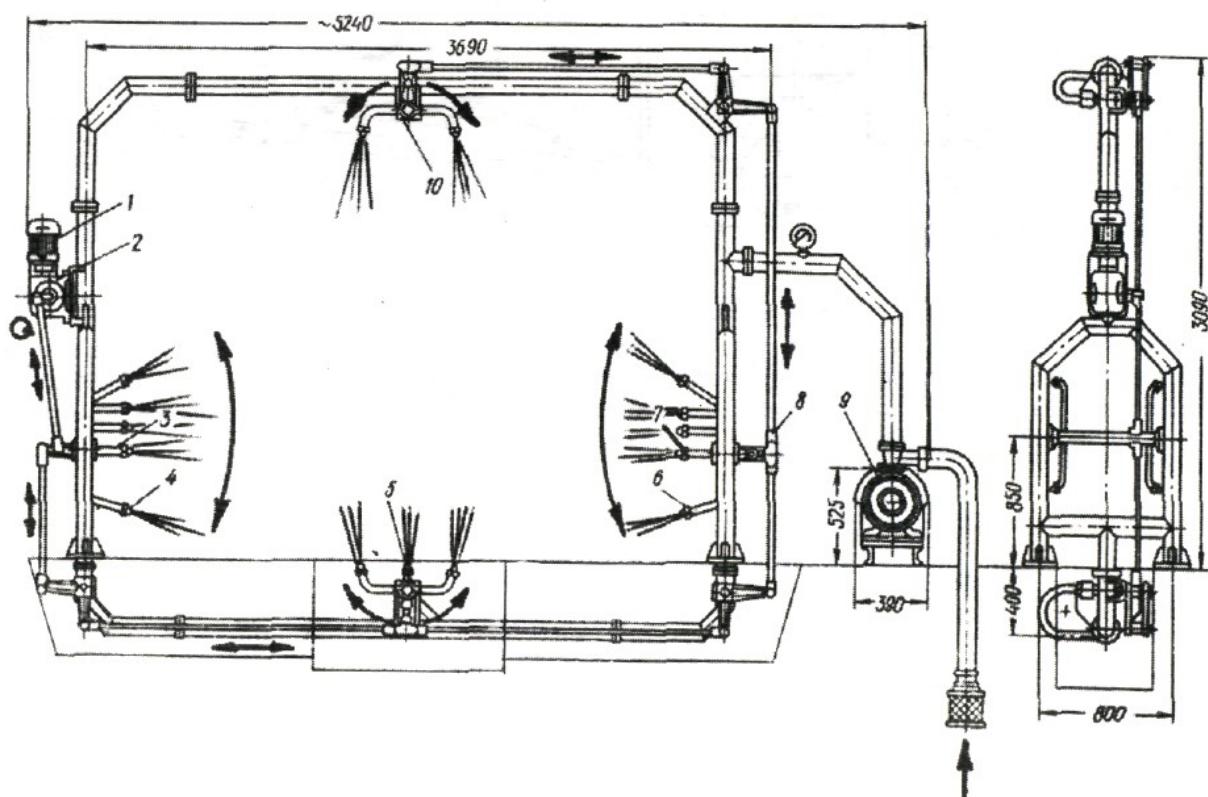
Моечная установка мод. 1114. Секция окончательного обмыва (вид спереди и сбоку): 1 - электродвигатель привода коллекторов; 2 - червячный редуктор; 3 и 7 - боковые качающиеся коллекторы; 4 и 6 - боковые неподвижные коллекторы; 5 - нижний качающийся коллектор; 8 - тяги привода качающихся коллекторов; 9 - насосная станция; 10 - верхний качающийся коллектор
